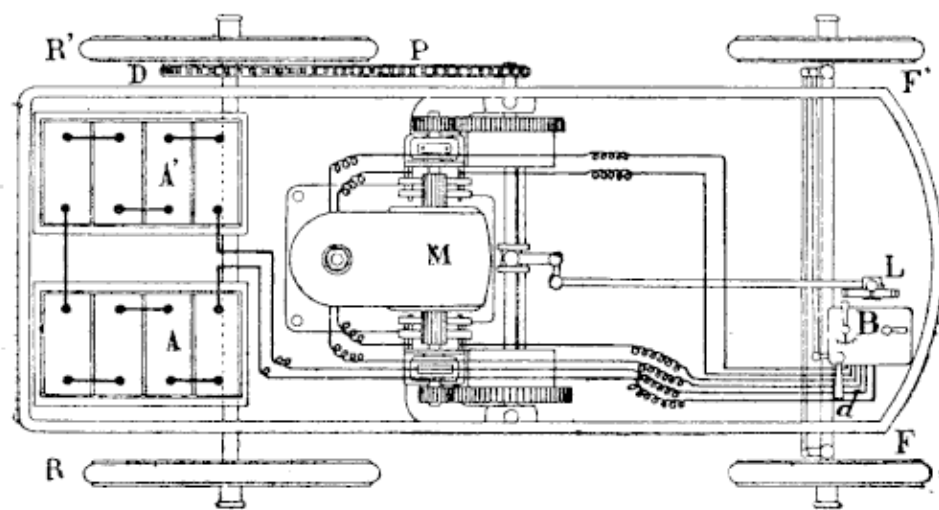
Plan de la Voiture MILDE-MONDOS.
